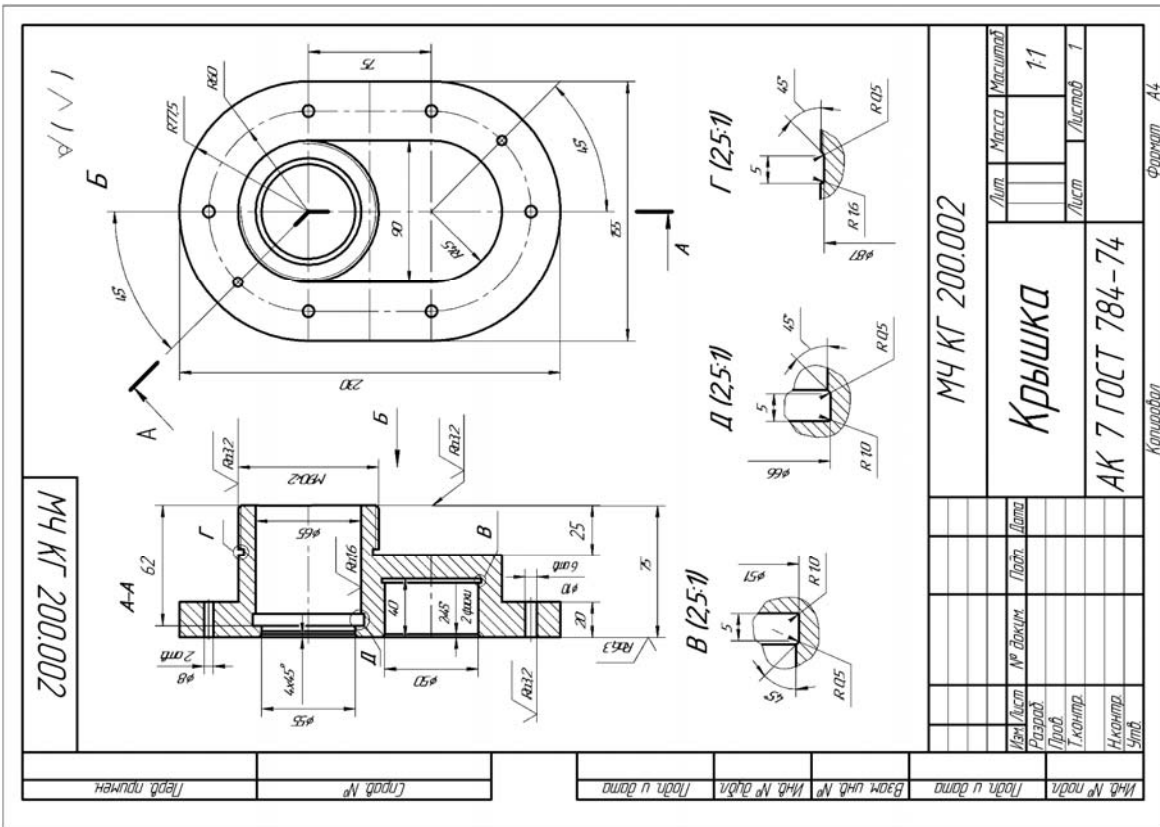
Рабочий чертеж «Крышка», позиция 2
